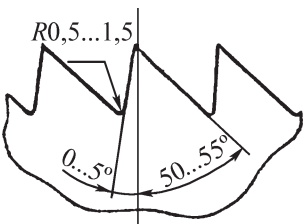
Форма и размеры зуба ножовочного станочного полотна
